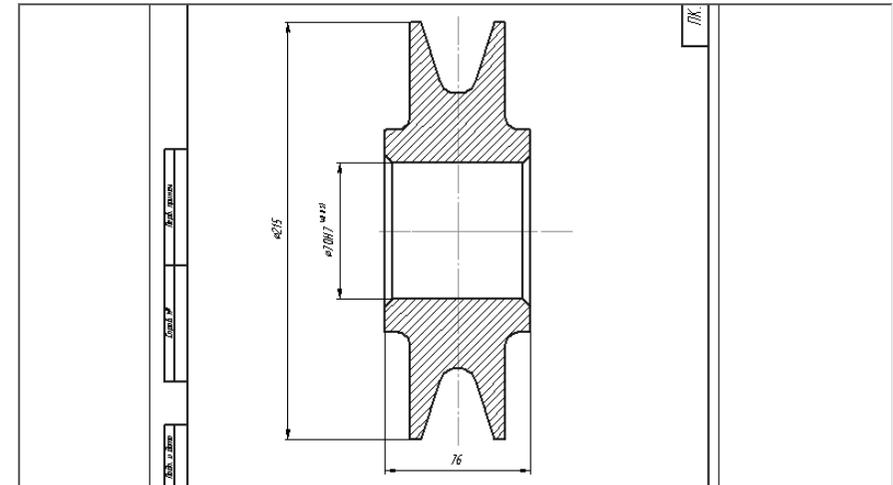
Представление Ролика с удаленными лишними размерами и обозначениями шероховатости
